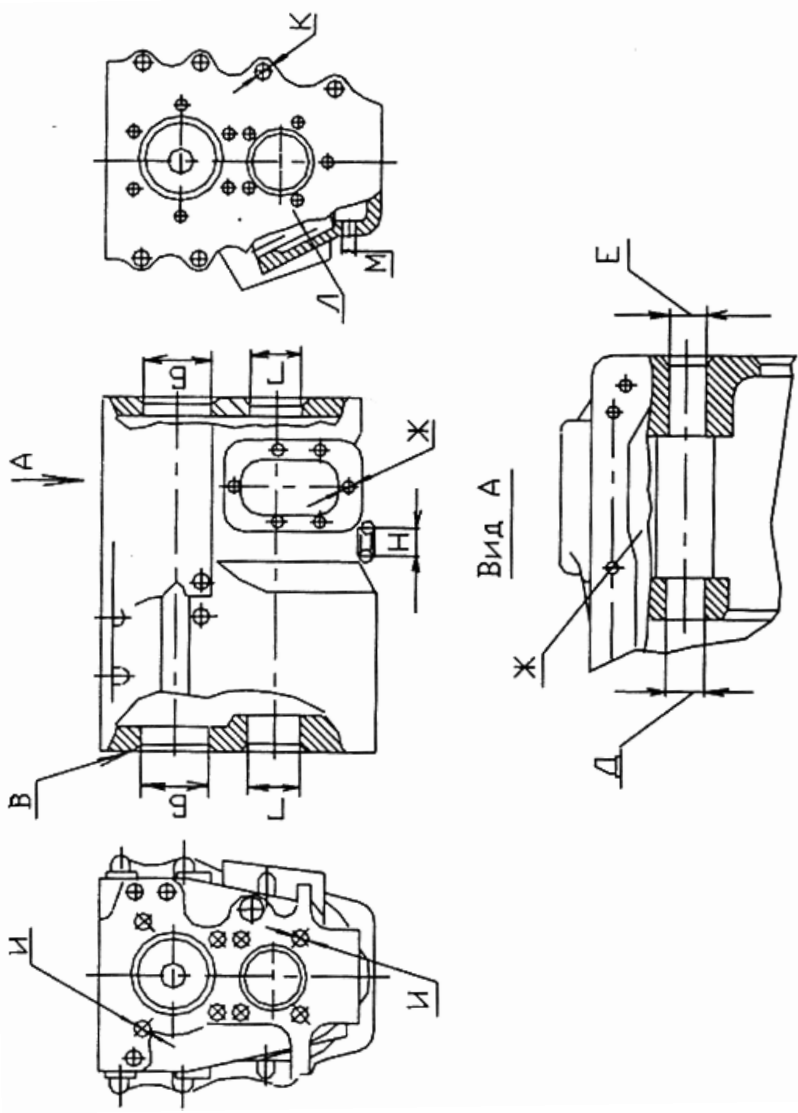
Картер коробки передач автомобиля КамАЗ
